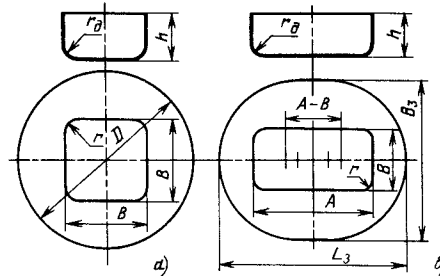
Контур заготовки для вытяжки высоких коробчатых деталей (см. рис. 3, область Ic): а — квадратной; б — прямоугольной
